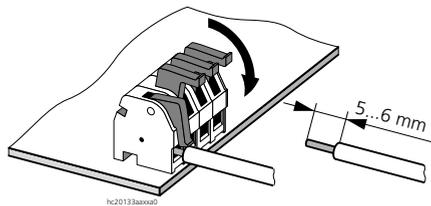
Connessione dei fili di collegamento con il PBX
